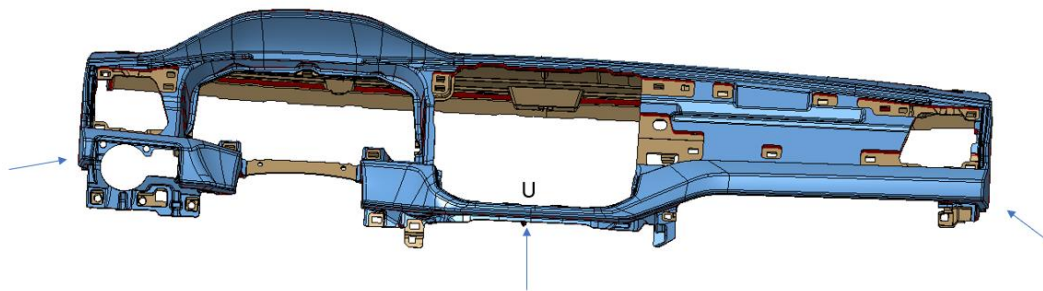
Salpicadero con zonas donde colocar apoyos.
